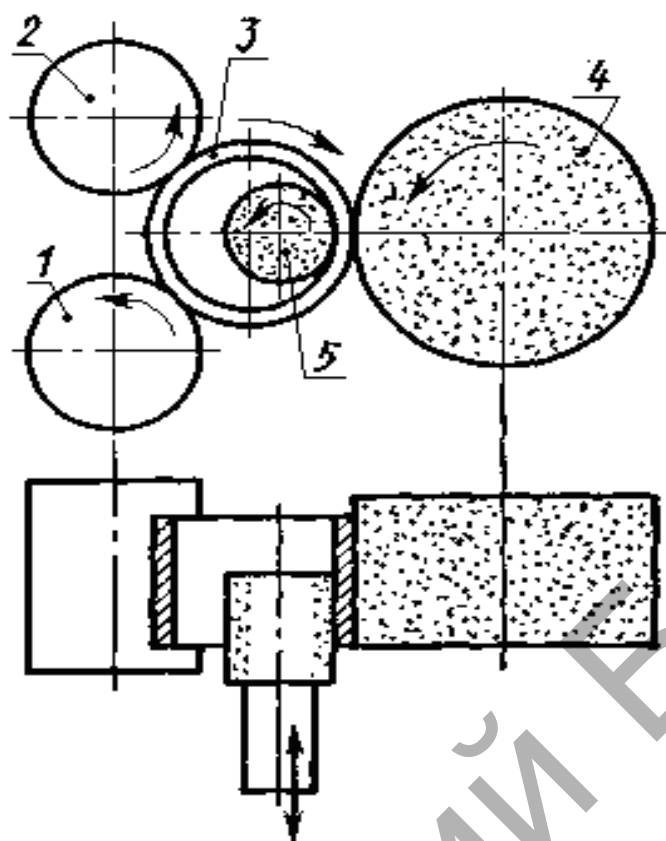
Схема внутреннего бесцентрового шлифования
